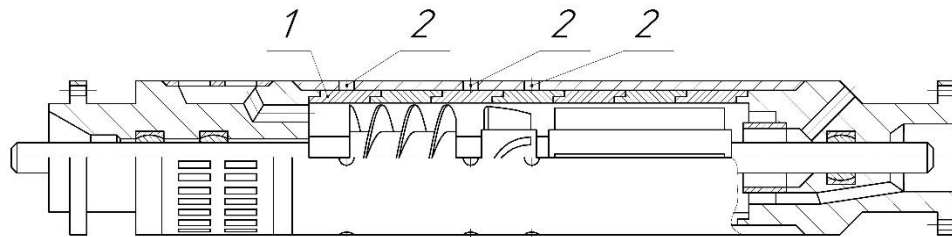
Модернизированный центробежный газосепаратор конструкции П.Д. Ляпкина:
